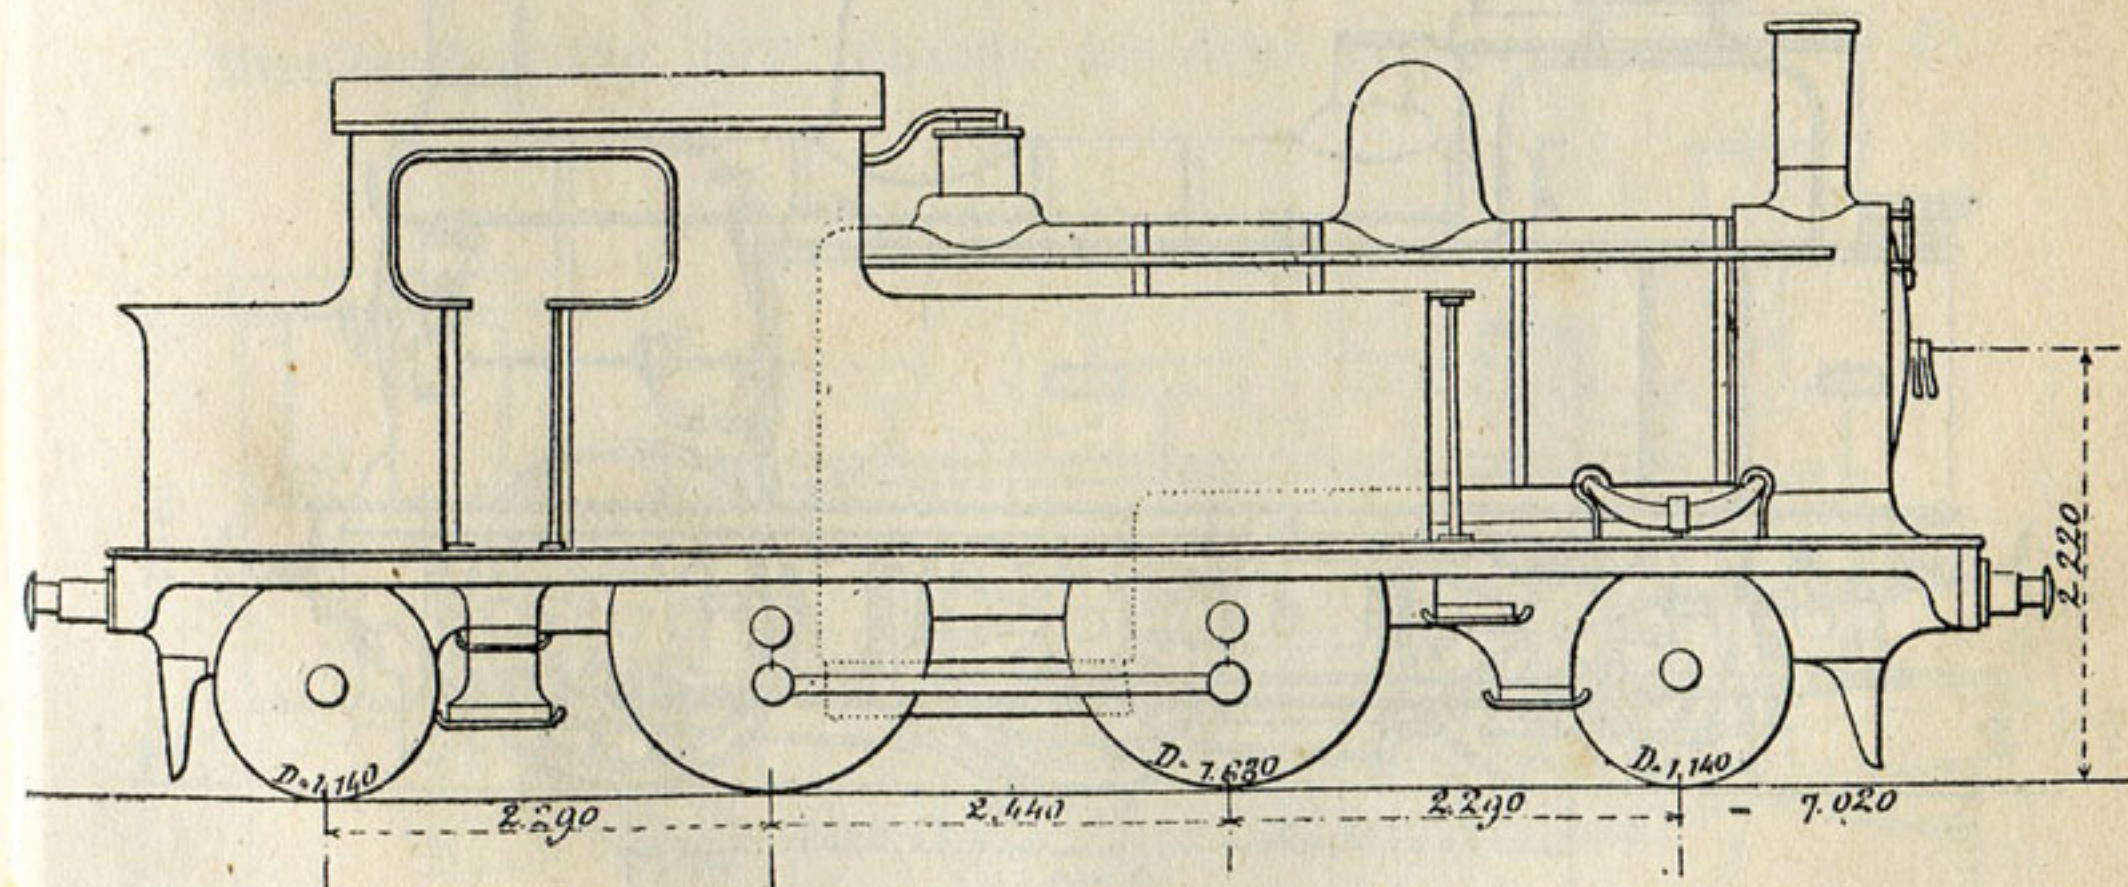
Locomotive-tender à 2 essieux couplés, du Great Eastern railway, avec essieu porteur à chaque extrémité. D'après M. Morandière.
